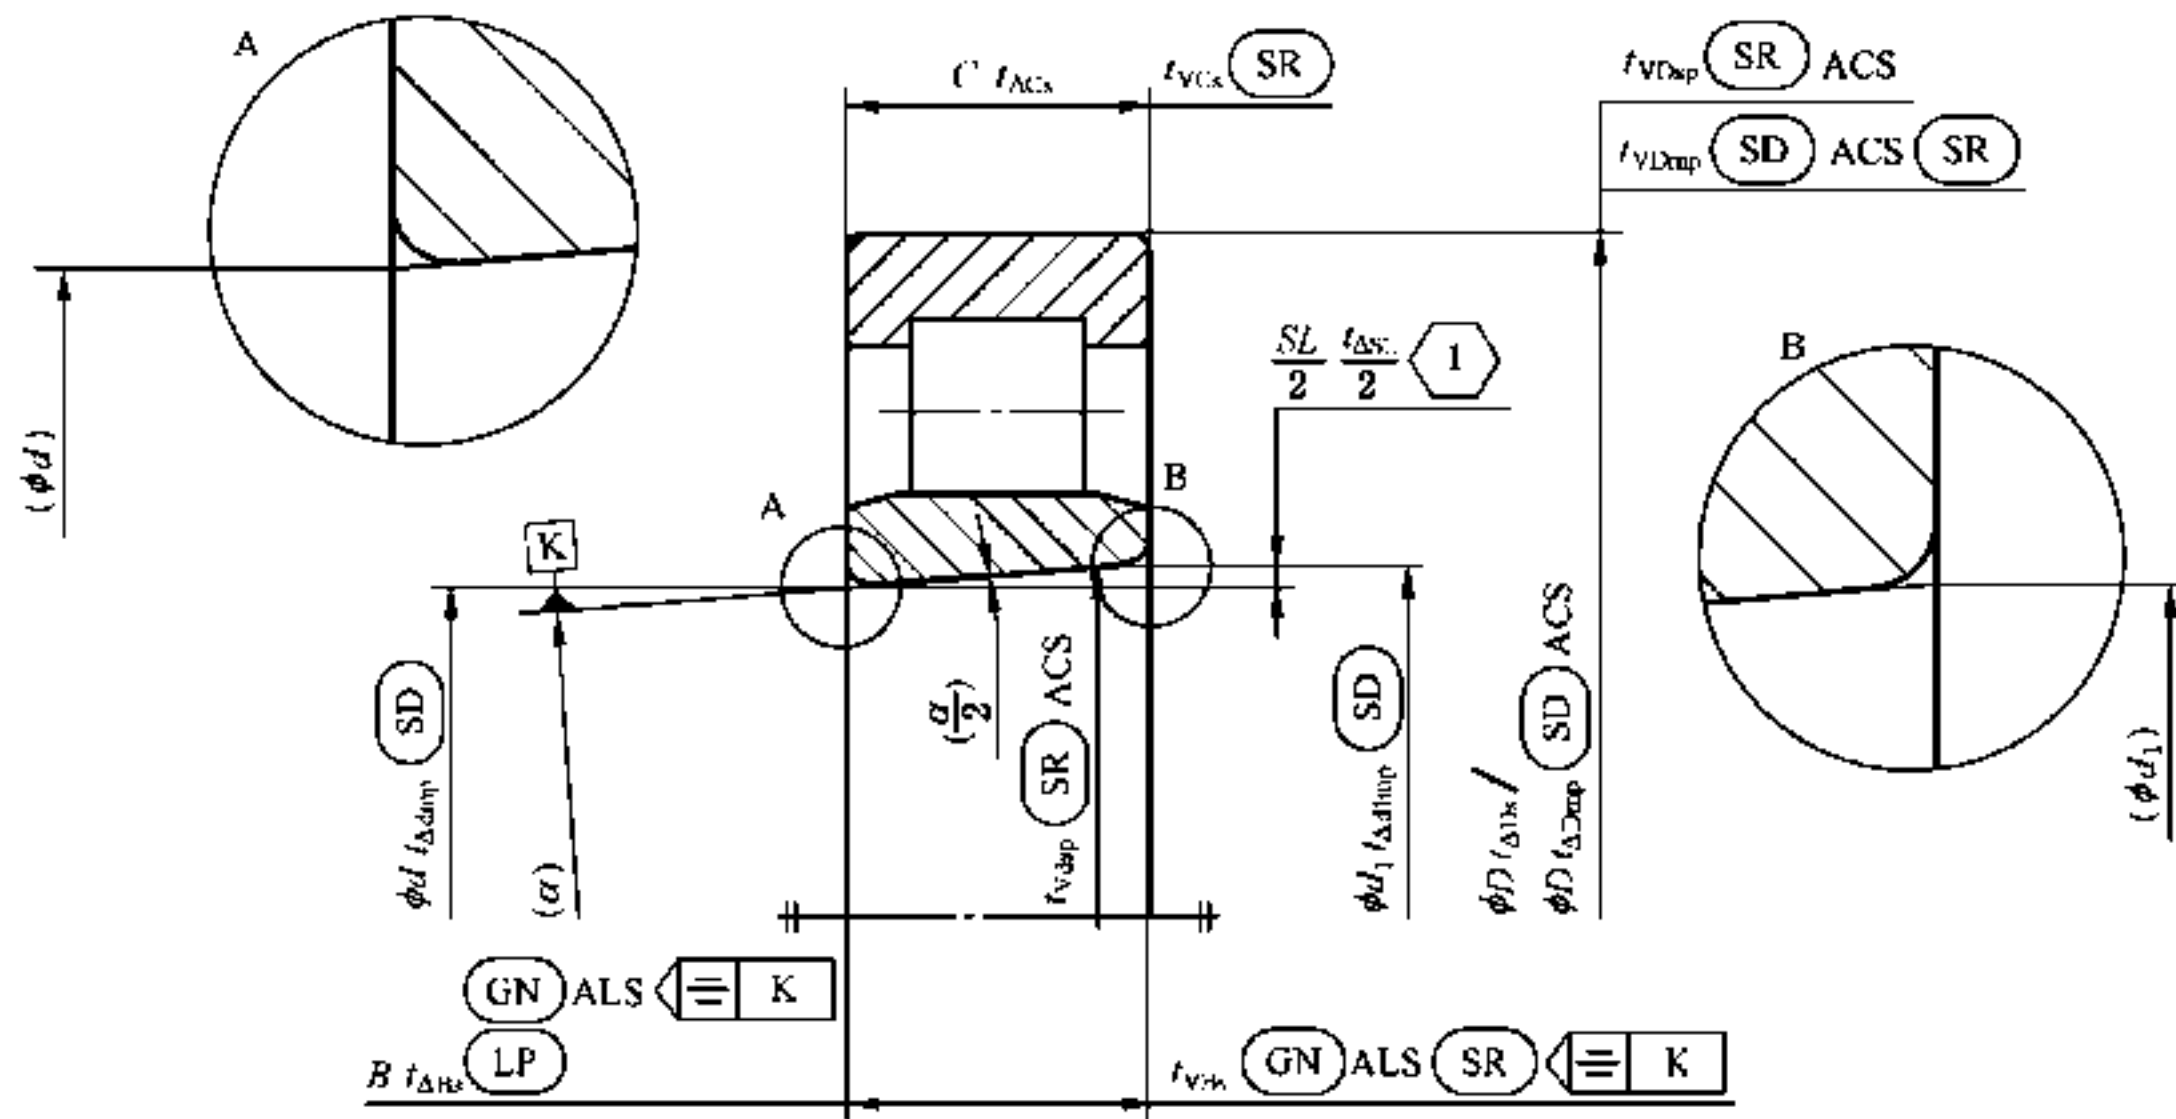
圆柱孔成套轴承的几何公差——单列角接触球轴承和圆锥滚子轴承
